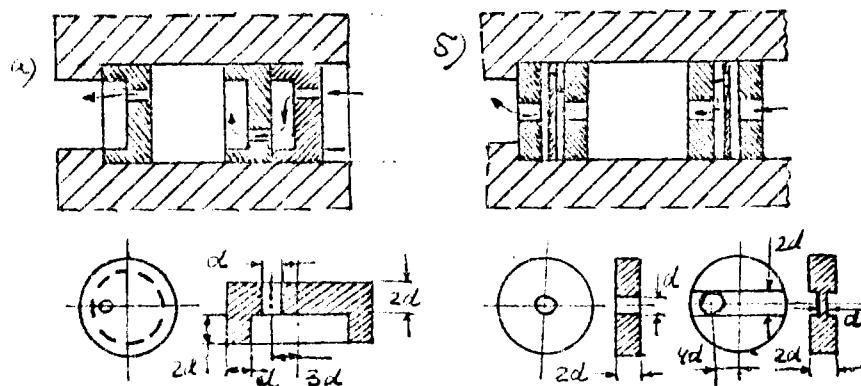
Пакетные дроссели с цилиндрическими насадками:
